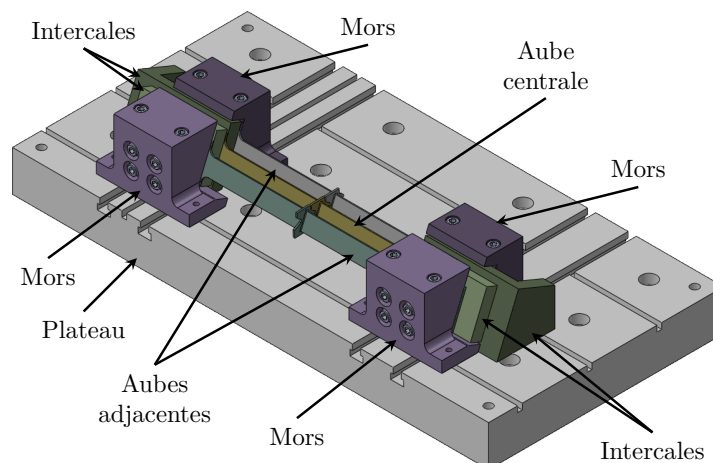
Vue globale des pièces du banc d'essai.
